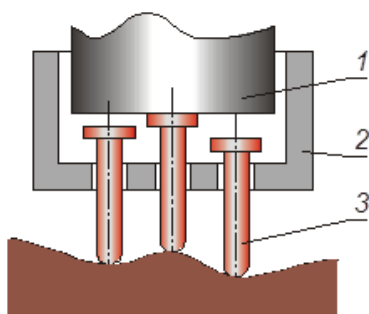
Схема рабочего узла многоэлементного инструмента для обработки сварных швов: 1 – волновод; 2 – обойма; 3 – деформирующие элементы
